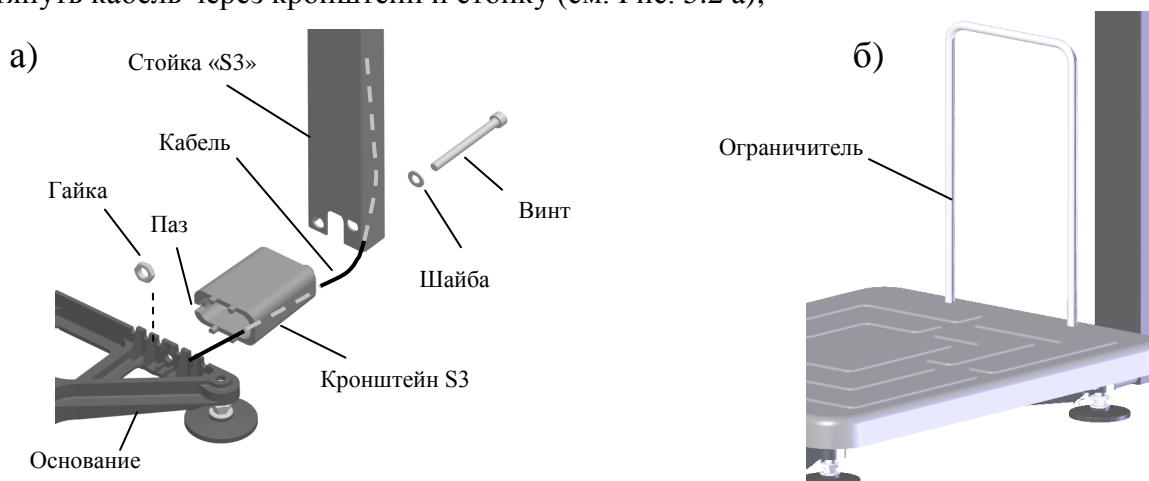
Крепление прямоугольной стойки к модулю ТВ-S\
